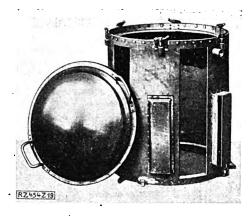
Mittels Punktschweißung hergestelltes Scheinwerfergehäuse
